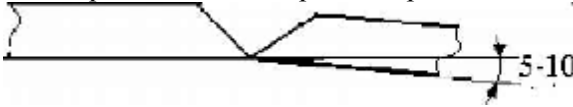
Схема розташування деталей перед зварюванням
